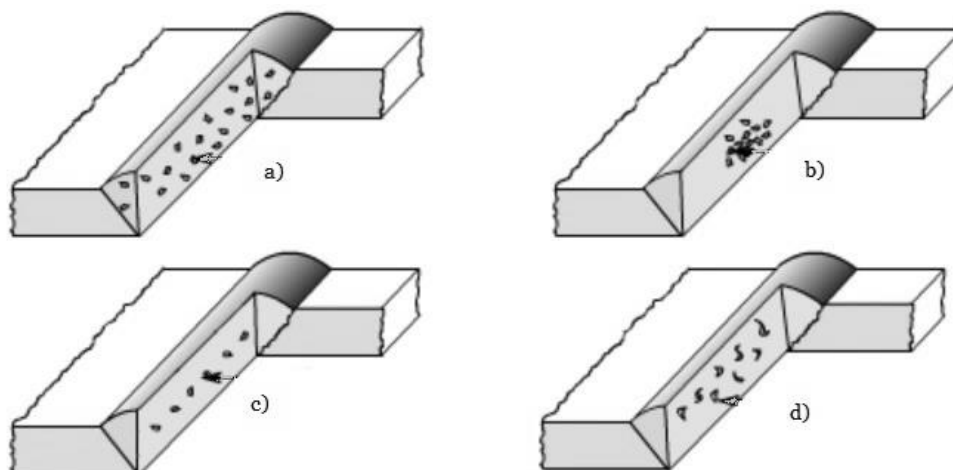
Tipos de porosidades que pueden presentarse en soldadura
